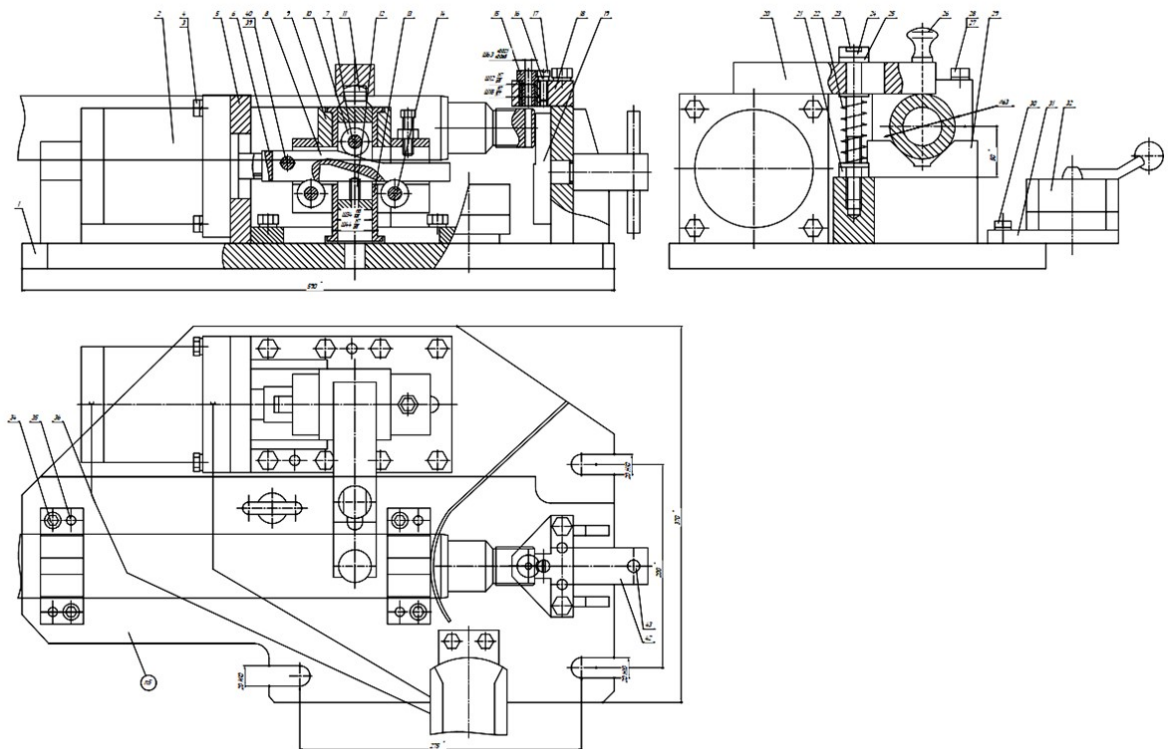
Загальний вигляд пристрою для свердлування
